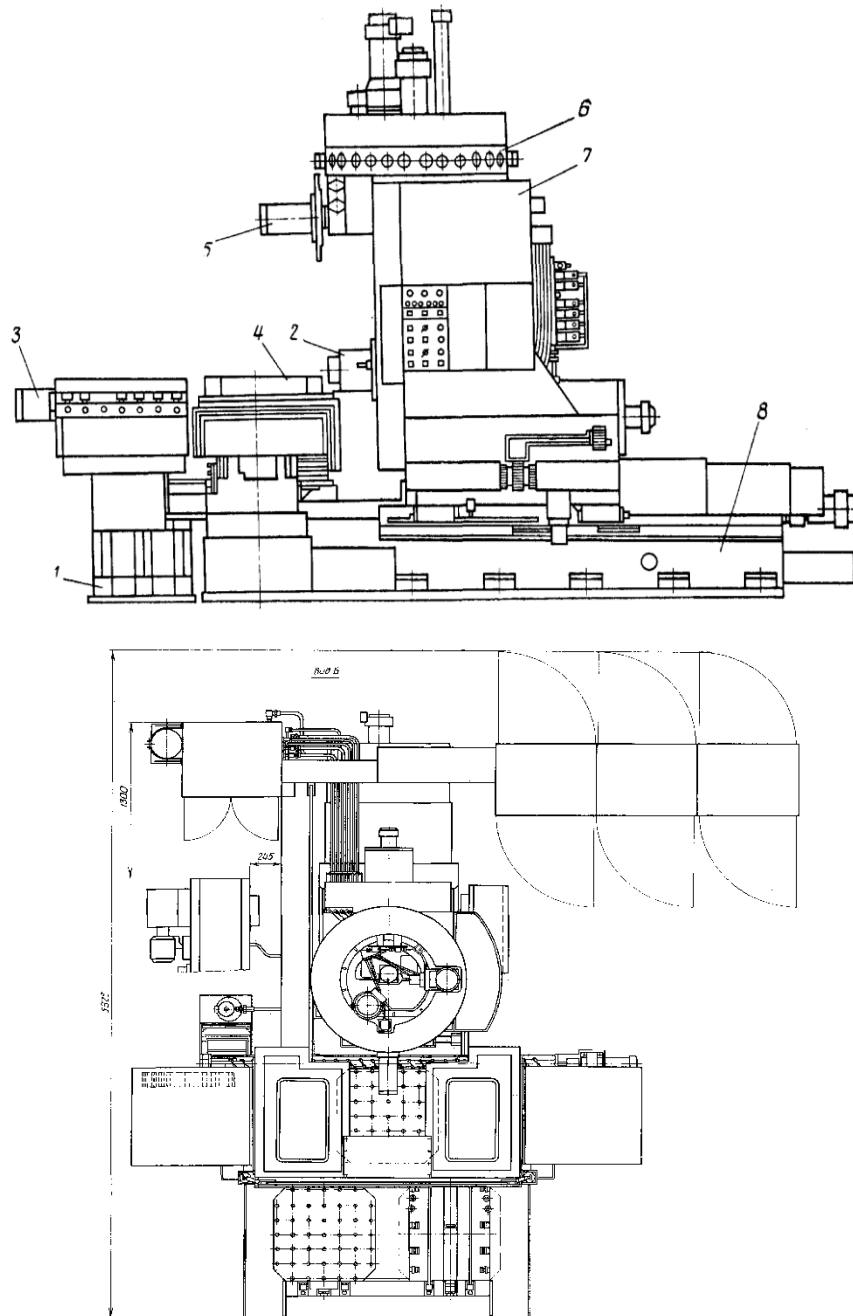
Зовнішній вигляд багатоцільового верстата MAST\_MM855\_S24
